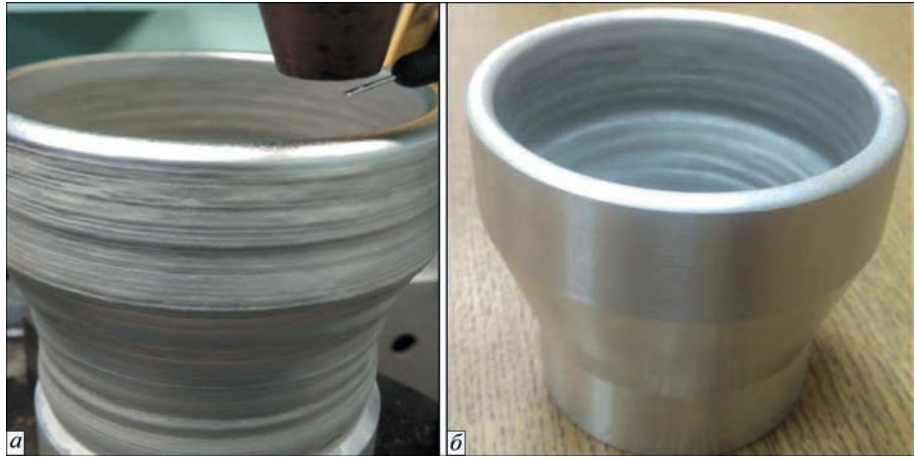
Перехідник з алюмінієво-магнієвого сплаву 1580, виготовлений АПДН на постійному струмі зворотної полярності [17]: зовнішній вигляд після 3D друку (а) та після механічної обробки (б)
